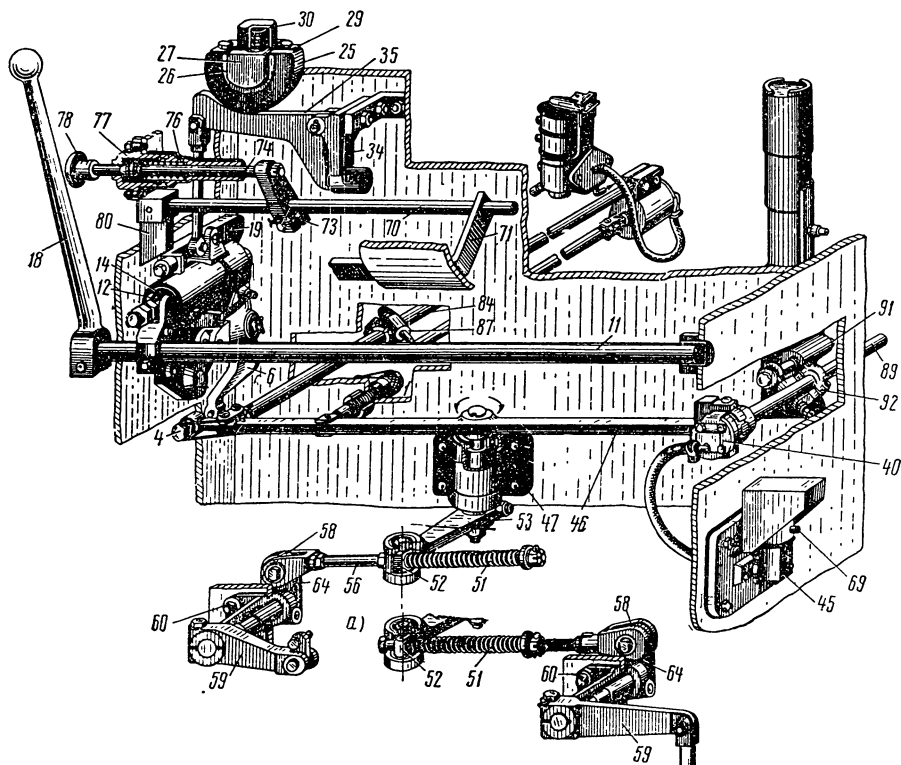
Механизм управления дизелем (обозначения см. на рис. 109): а — расположение стопорной тяги и рычагов при установке регулятора числа оборотов с правой стороны дизеля
